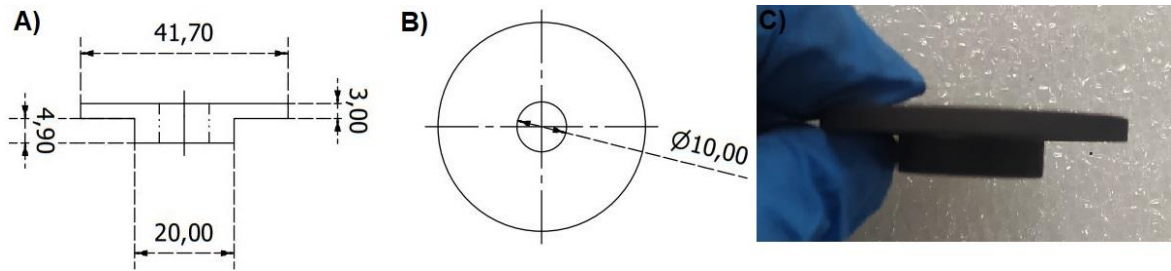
Escudo térmico: a) Plano vista lateral, b) Plano vista superior, c) Foto vista lateral. Las dimensiones están en milímetros.
